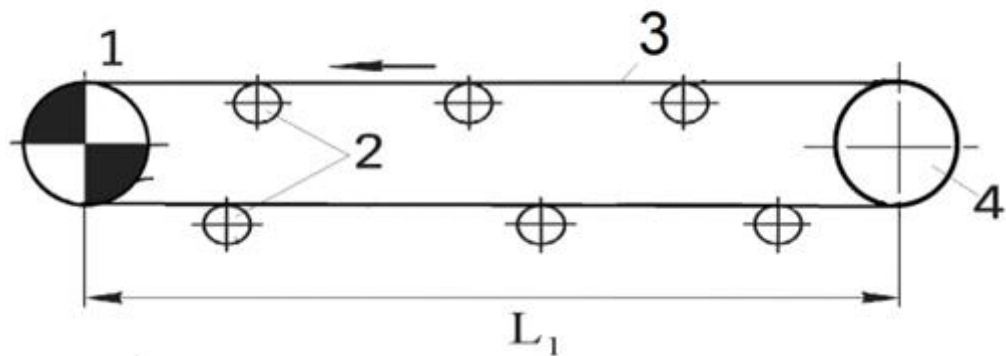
Схема конвеєру: 1 – привідний барабан; 2 – ролюкоопори; 3 – стрічка; 4 – натяжний барабан
